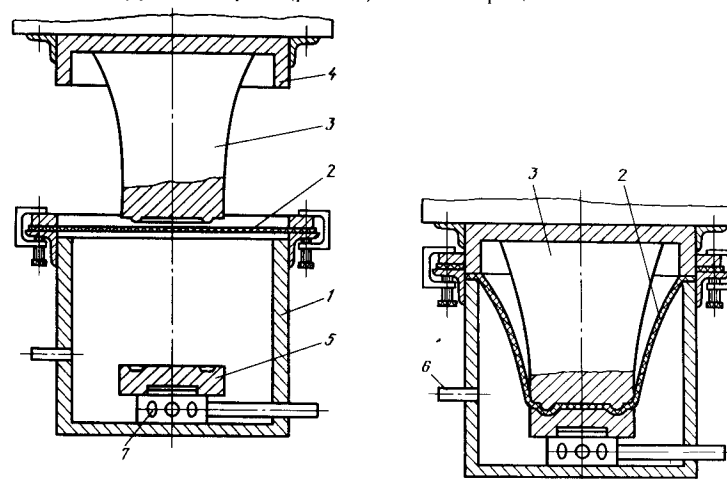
Схема комбинированной формовки в «упругой» матрице
